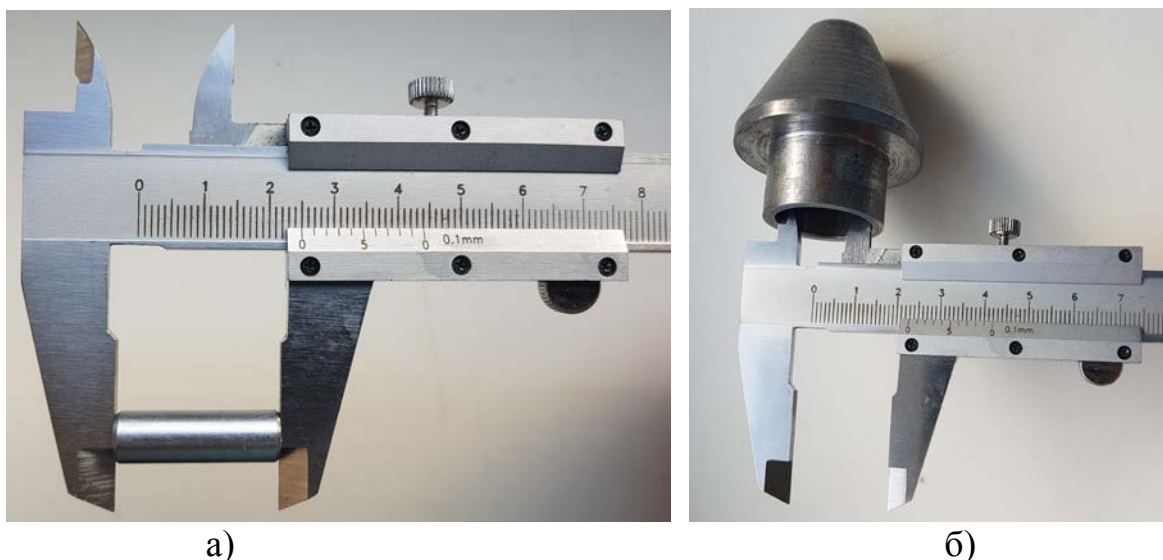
Измерение штангенциркулем наружного а) и внутреннего б) размеров детали
